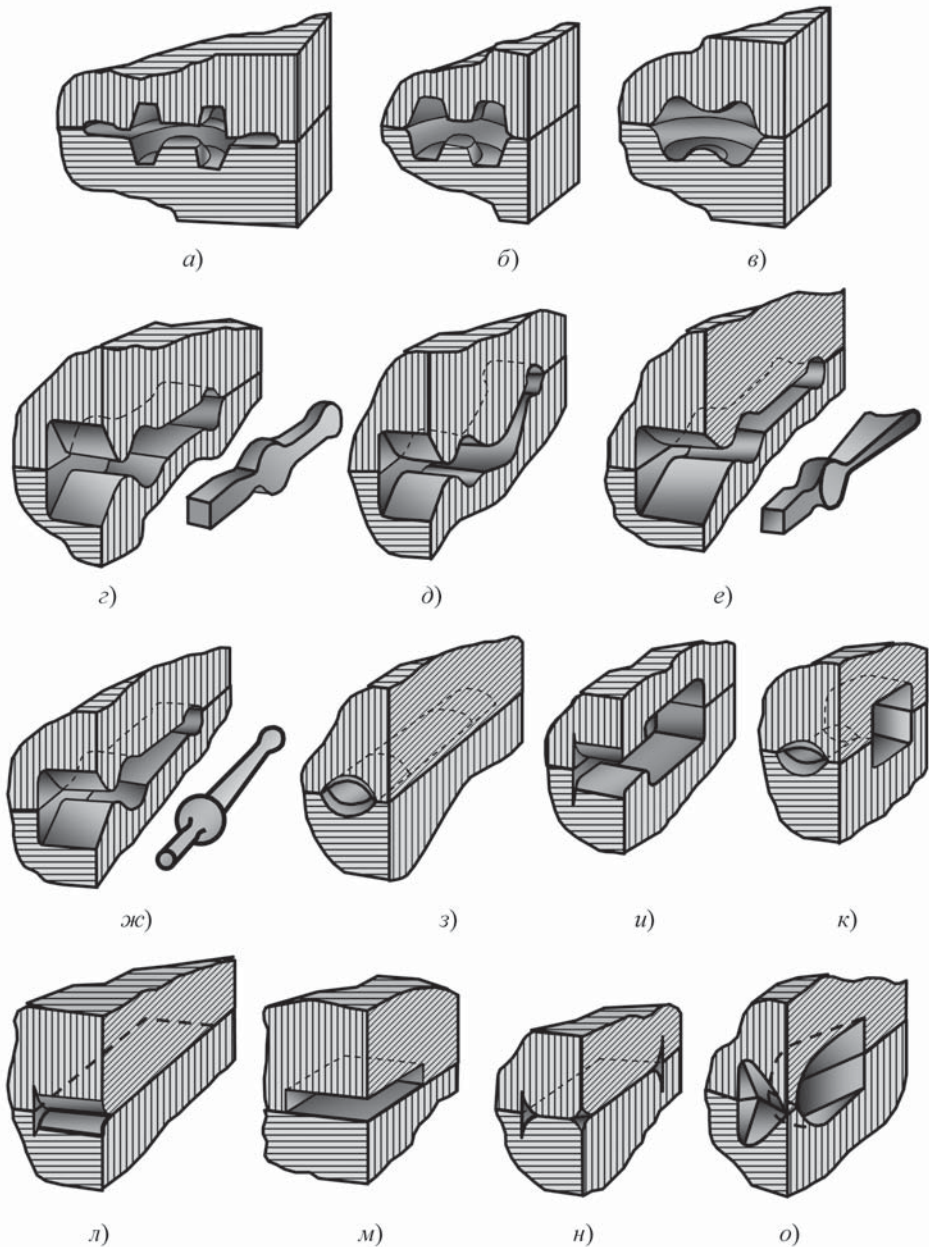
Заготовительные и штамповочные ручки молотового штампа:
